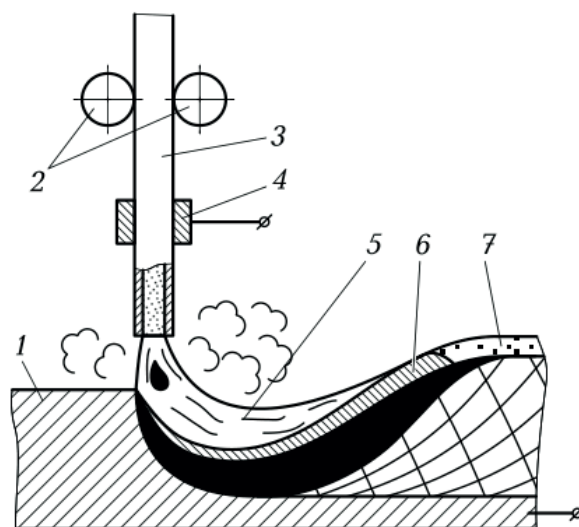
Схема дугового зварювання порошковим дротом: 1 – зварювана деталь; 2 – подаючі ролики; 3 – порошковий дріт; 4 – ковзний струмопідвід; 5 – дуга; 6 – розплавлений шлак; 7 – затверділий шпак
